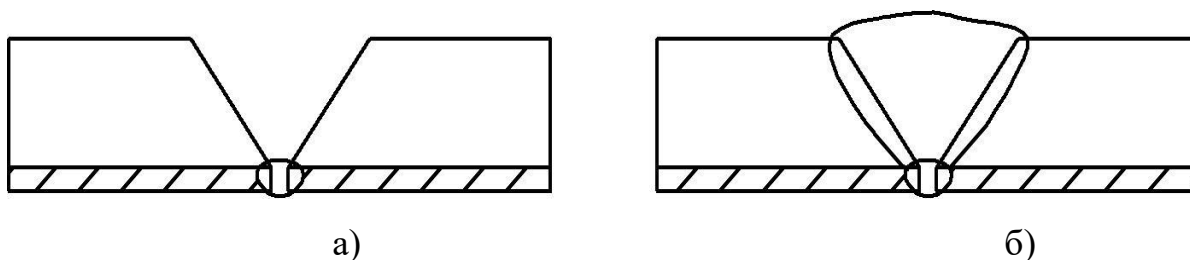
Последовательность наложения швов при односторонней сварке
